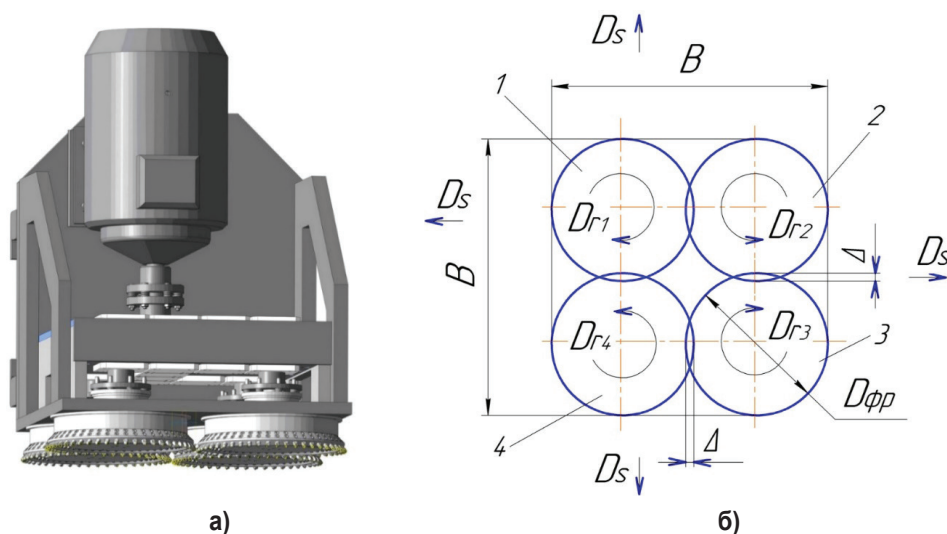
3D-модель АФГ з чотирма торцевими фрезами (а) та схема розташування фрез (б): 1, 2, 3, 4 – фрези; $D_{фр}$ – діаметр фрез; D_{r1} , D_{r2} , D_{r3} , D_{r4} – напрямки обертання шпинделів; B – максимально можлива ширина фрезерування; Δ – перекриття траєкторій різальних ножів фрези; D_s – можливий напрям робочої подачі
